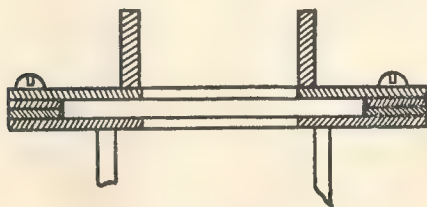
Die Einspannvorrichtung für die Glimmermembran.
